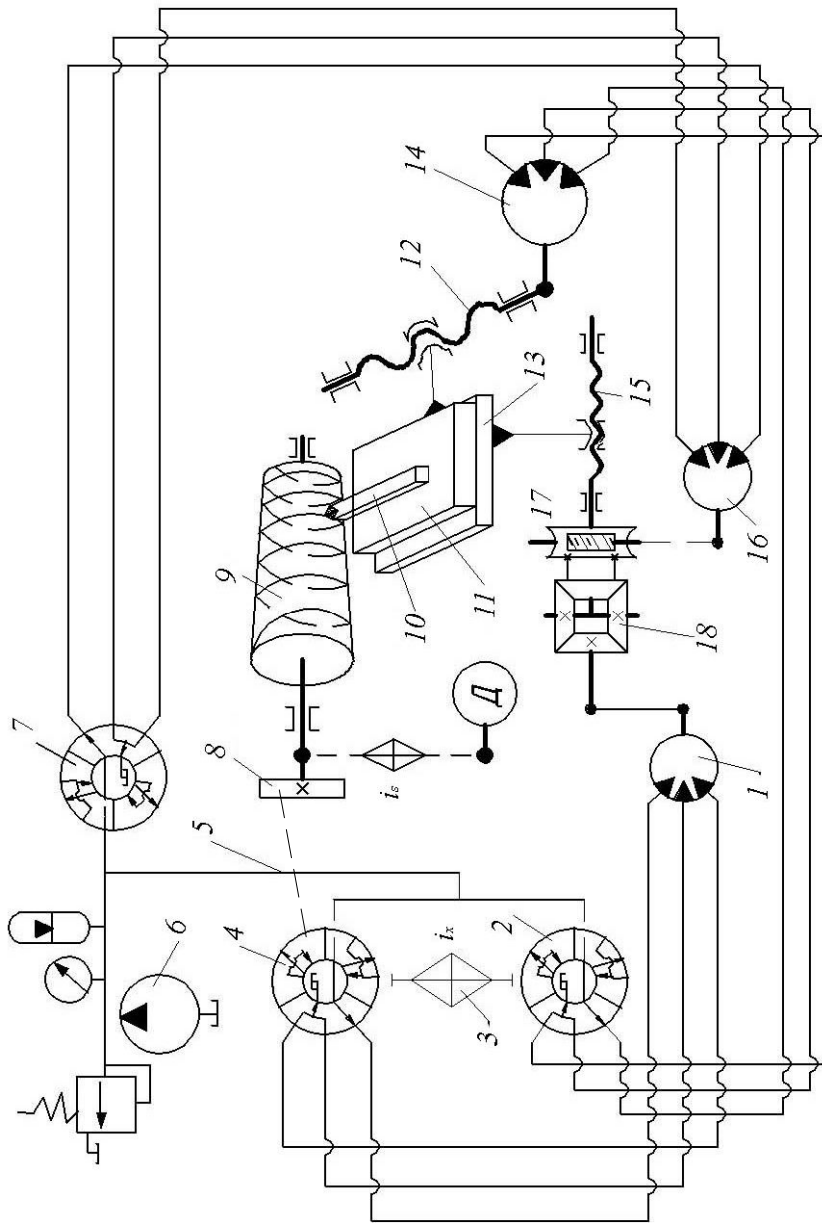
Структурная схема резбонарезного станка с гидравлическими внутренними связями для нарезания конических резьб с неравномерным шагом
